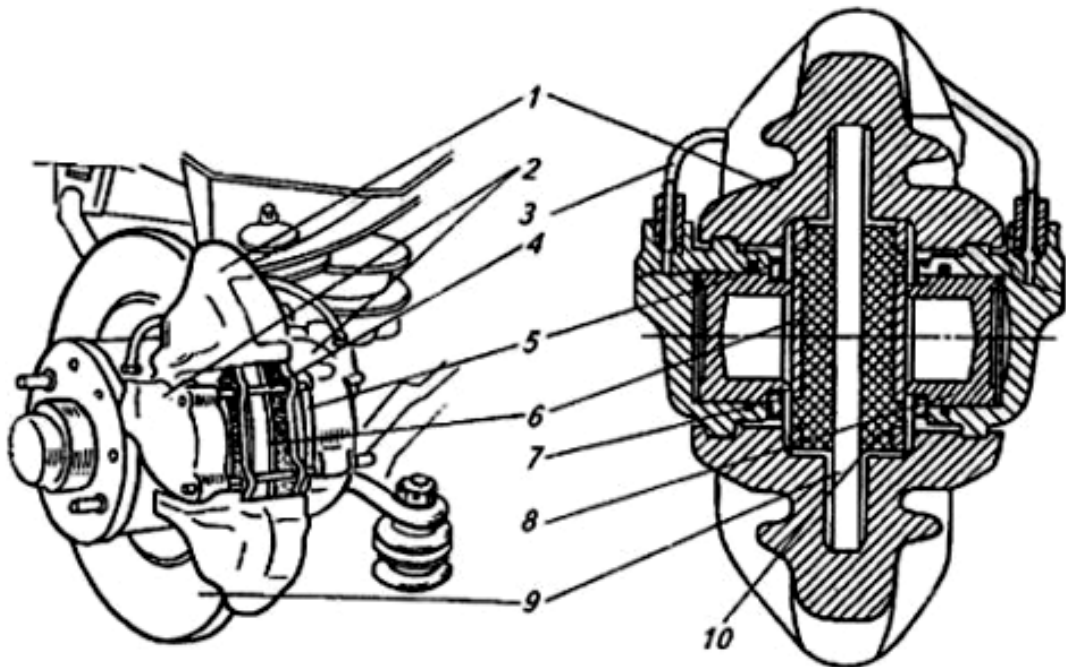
Дисковый тормозной механизм с фиксированной скобой: 1 - скоба; 2 - тормозные цилиндры; 3 - трубопровод; 4 - палец; 5 - защитный чехол; 6 - тормозная колодка; 7 - уплотнительное кольцо; 8 - поршень; 9 - диск; 10 - фрикционная накладка
